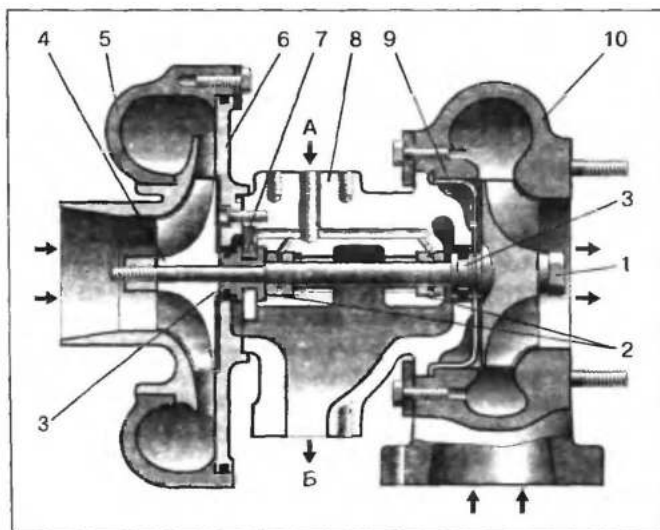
Схема турбокомпрессора: 1 — ротор с колесом турбины; 2 — подшипник ротора; 3 — уплотнения ротора; 4 — колесо компрессора; 5 — корпус компрессора; 6 — корпус уплотнения компрессора; 7 — гидродинамический подпятник; 8 — корпус подшипников; 9 — кожух уплотнения; 10 — корпус турбины; А — вход масла; Б — слив масла
